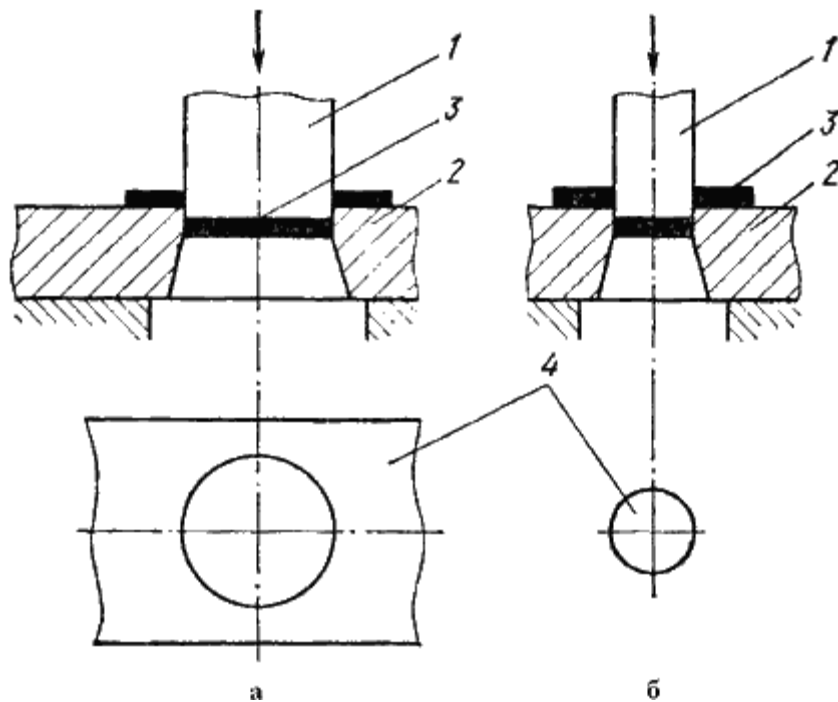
Схема процессов вырубki (а) и пробивки (б)
